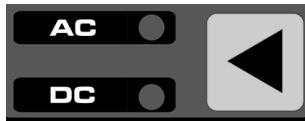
Seleção modo de soldagem TIG AC/DC
